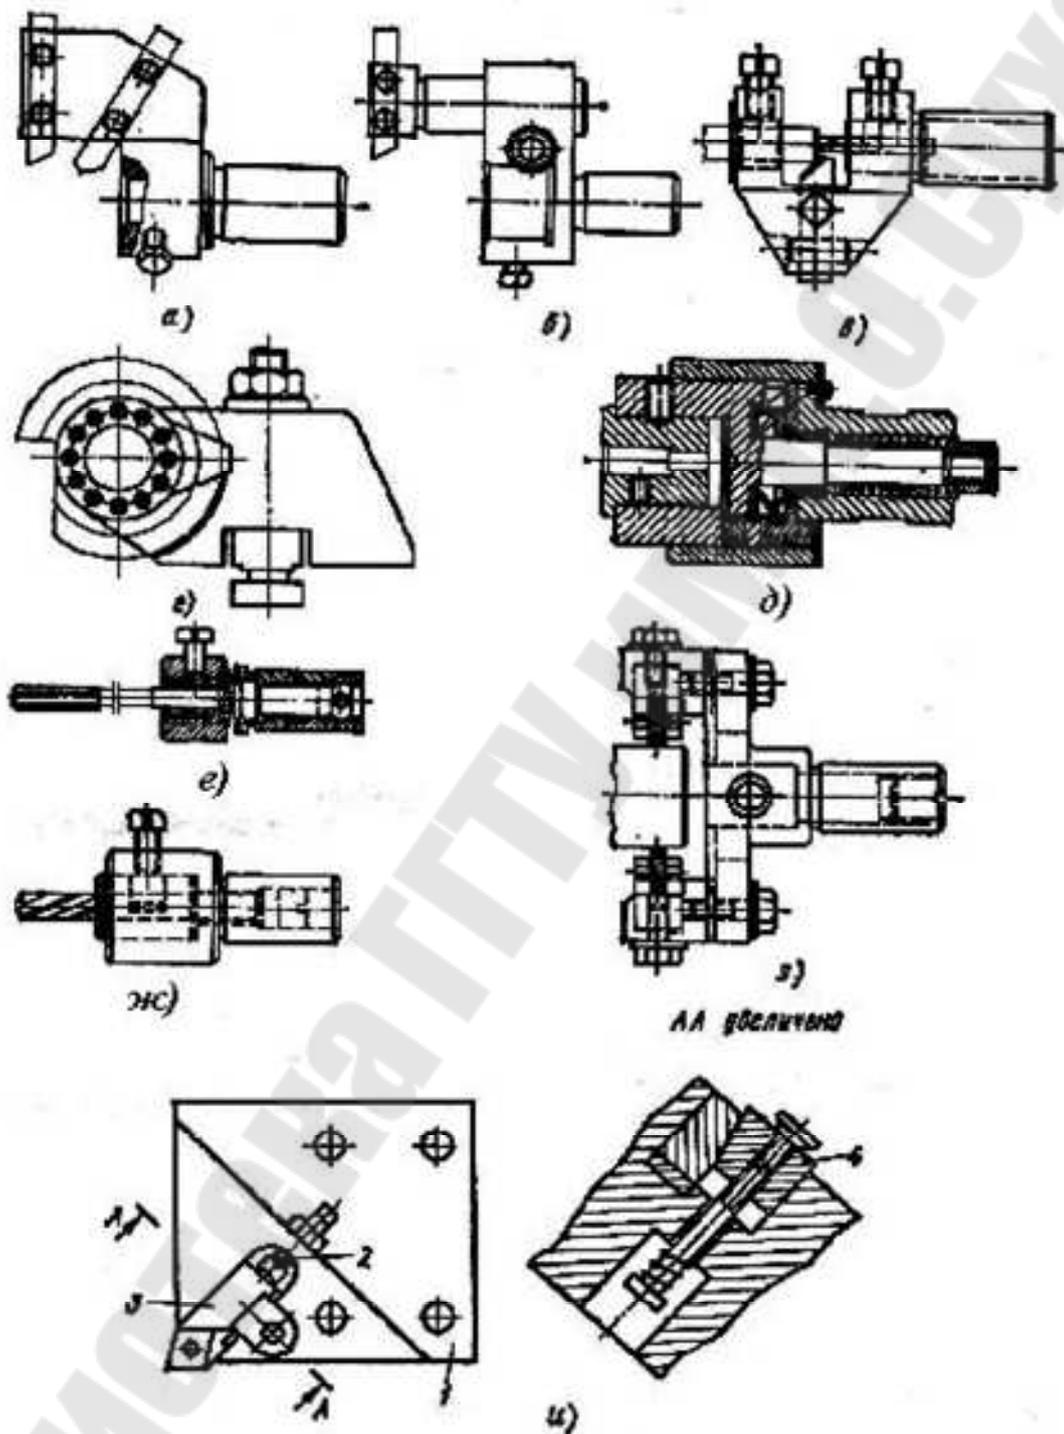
Эскизы державок для установки и закрепления инструментов: *а* - радиальная двухрезцовая; *б* - для обточки длинных заготовок; *в* - с направляющей втулкой; *г* - для круглого резца правого суппорта; *д* - для метчика; *е* - для развёртки; *ж* - для сверла; *з* - для накатных роликов; *и* - для крепления резца-вставки с неперетачиваемой твёрдосплавной пластинкой
